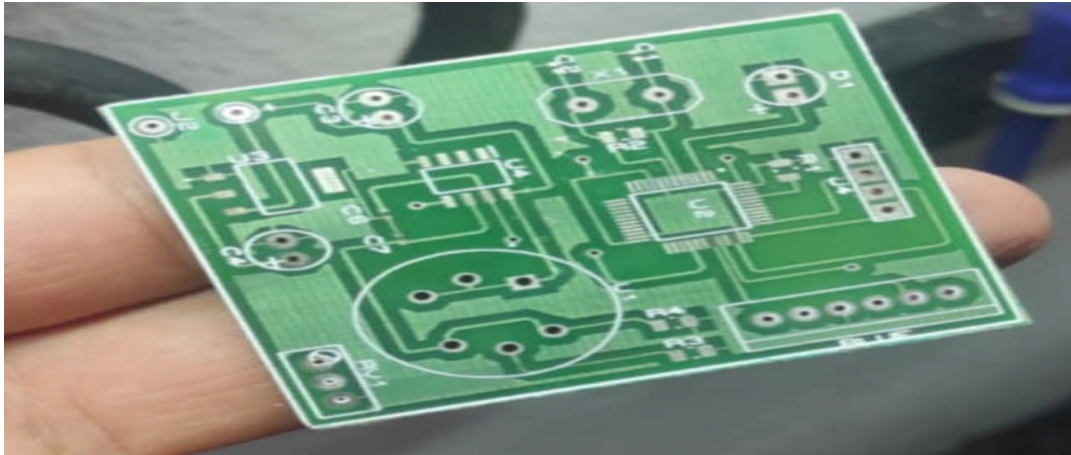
Les deux cartes après l'impression et début de la soudure.
